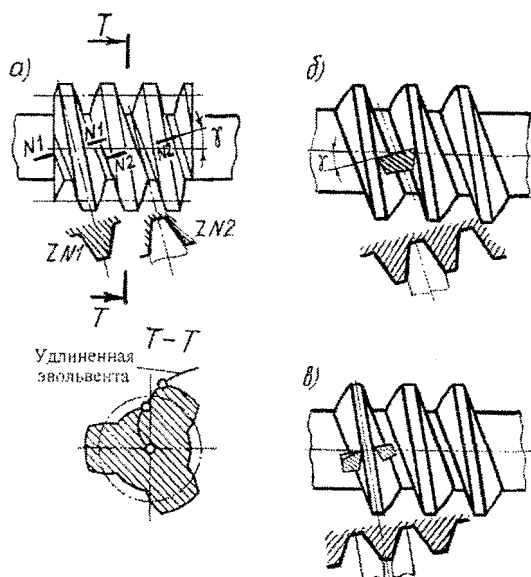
Конволютный червяк ZN (а) и схемы установки резцов с прямолинейным профилем: б – двустороннего резца для нарезания витка червяка ZN2; в – односторонних резцов для нарезания витка червяка ZN1
